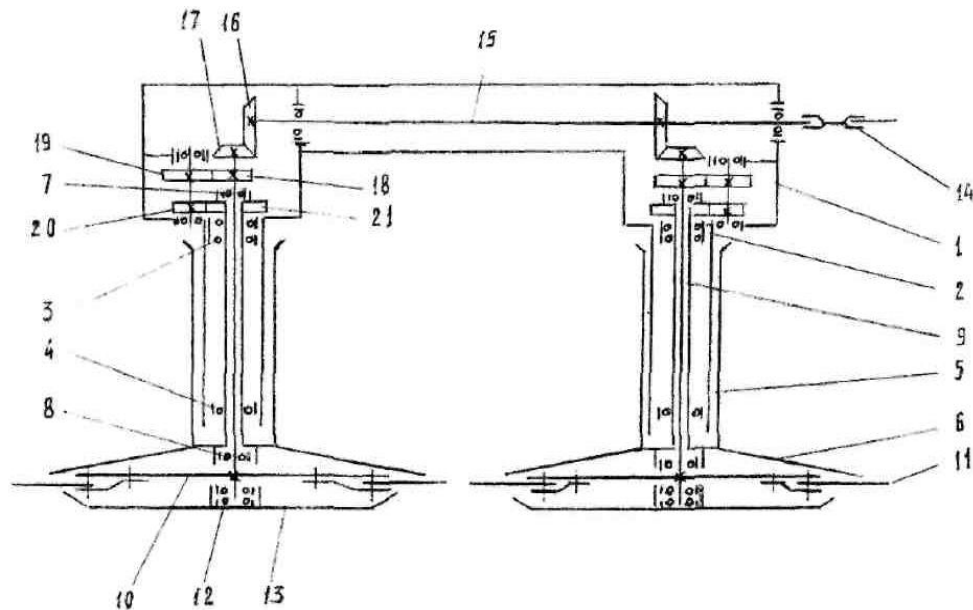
Кінематична схема косарки ротаційної з приводом транспортуєчого ротора за допомогою зубчастого редуктора
